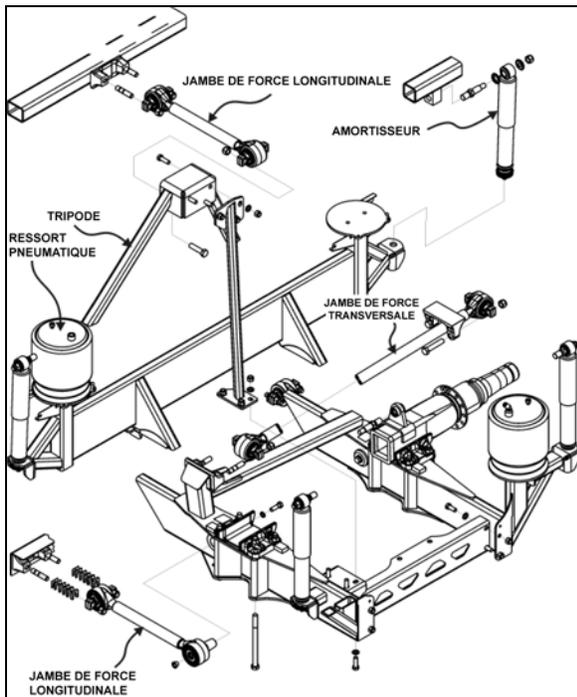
ESSIEU MOTEUR, DÉTAILS DE LA SUSPENSION ARRIÈRE
